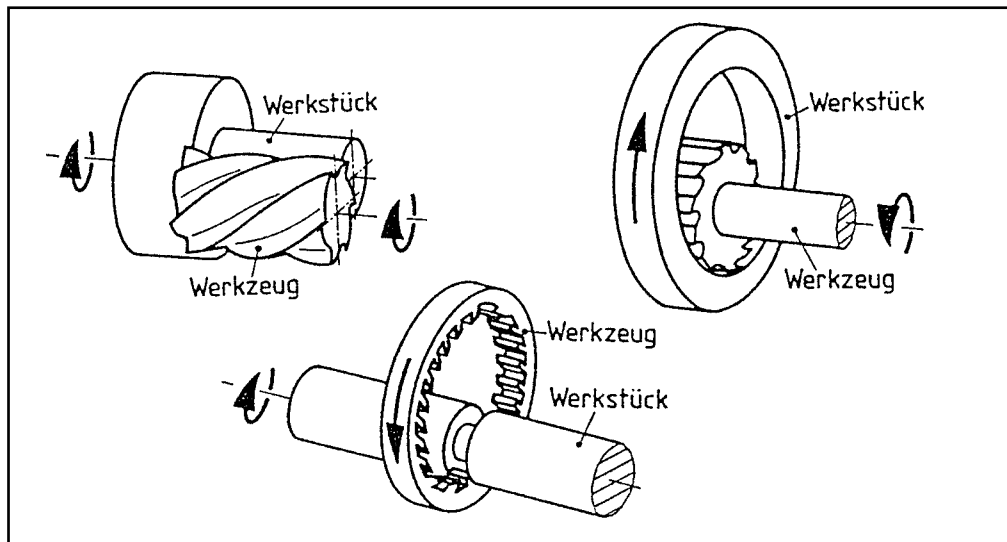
Werkzeug-Werkstück Kombinationen beim Rundfräsen /64/
